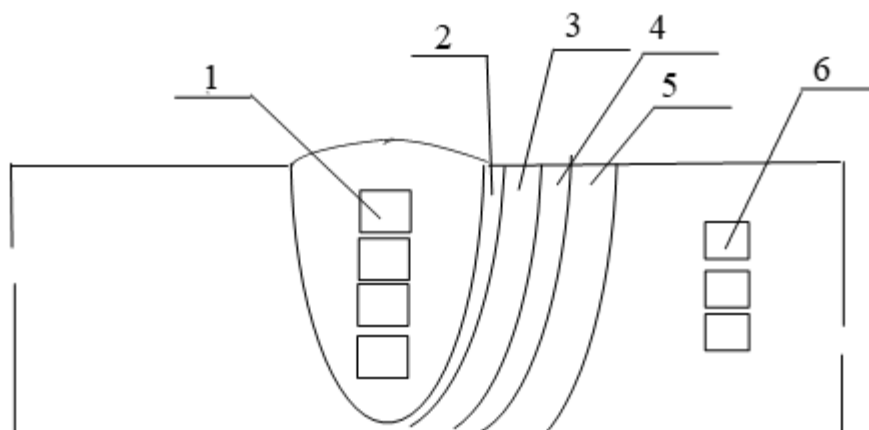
Схема виготовлення пластин із зварного з'єднання паропроводу:
